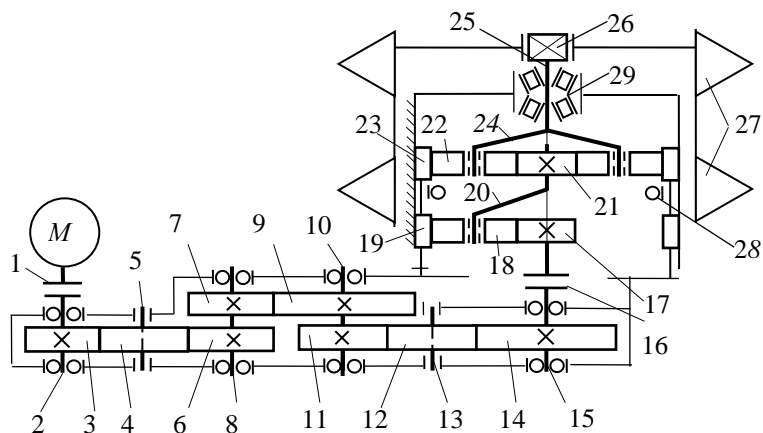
Кинематическая схема гидромеханического привода гусеницы комбайна CM2B-30P
